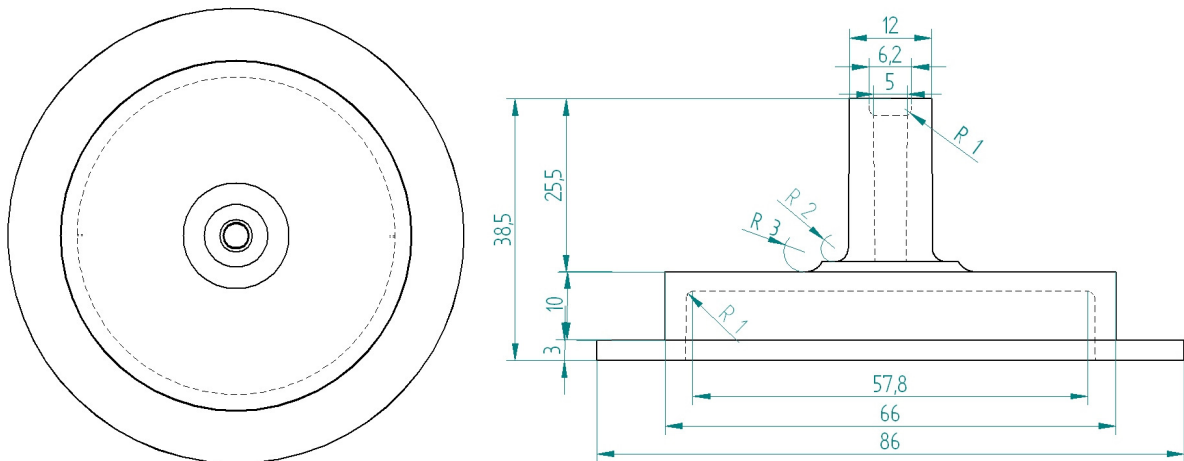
Bauteildemonstrator in unverrippter Ausführung
